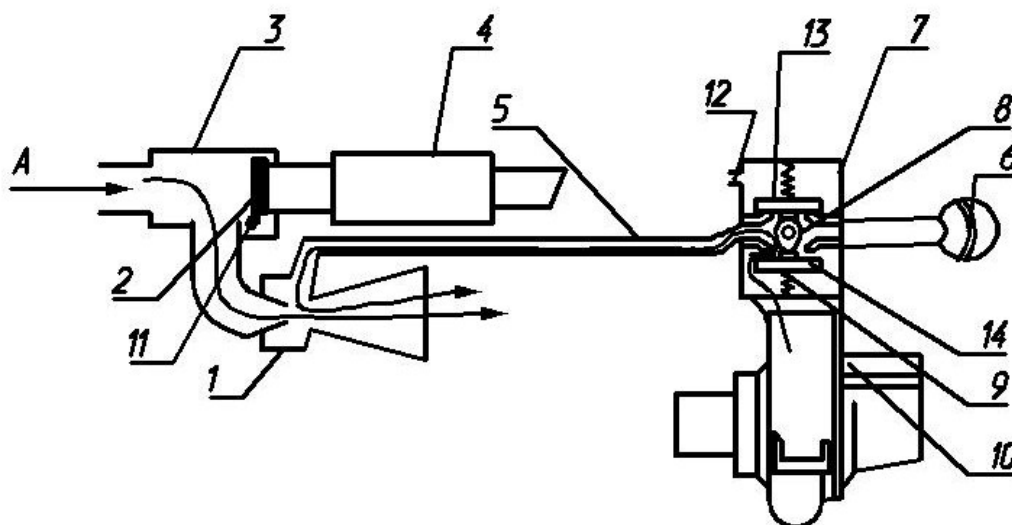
Схема вакуумной системы: газоструйный вакуумный аппарат включен, под действием атмосферного давления вода заполняет центробежный насос: 1-струйный насос; 2 - заслонка; 3 - корпус газоструйного вакуум-аппарата; 4 - глушитель; 5-труба 8 - валик; 9 - пружины; 10 - пожарный насос, 11 – ось заслонки; 12 – отверстие для сообщения с атмосферой; 13 – верхний клапан; 14 – нижний клапан; А – направление потока отработавших газов.
